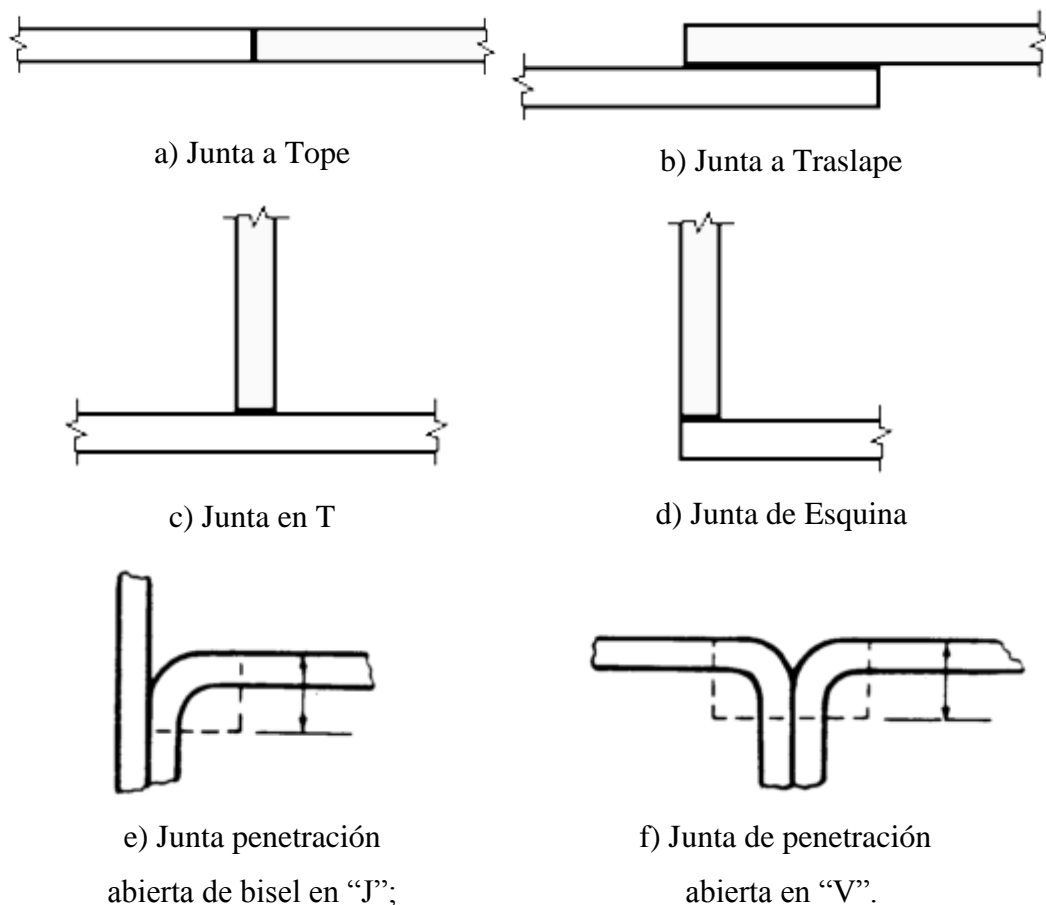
Tipos Básicos de Juntas Soldadas
